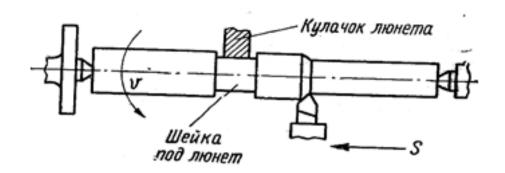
Схема обработки с помощью неподвижного люнета
